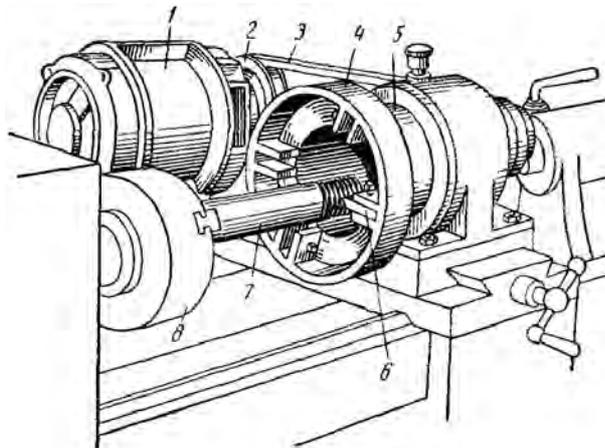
Приспособление для нарезания резьбы вращающимся резцом
